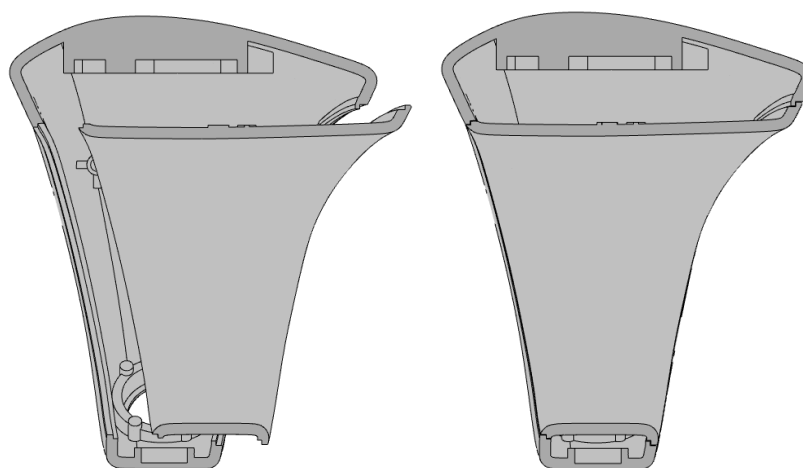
Позиционирование внутренней детали корпуса во внешнюю посредством выступа.
